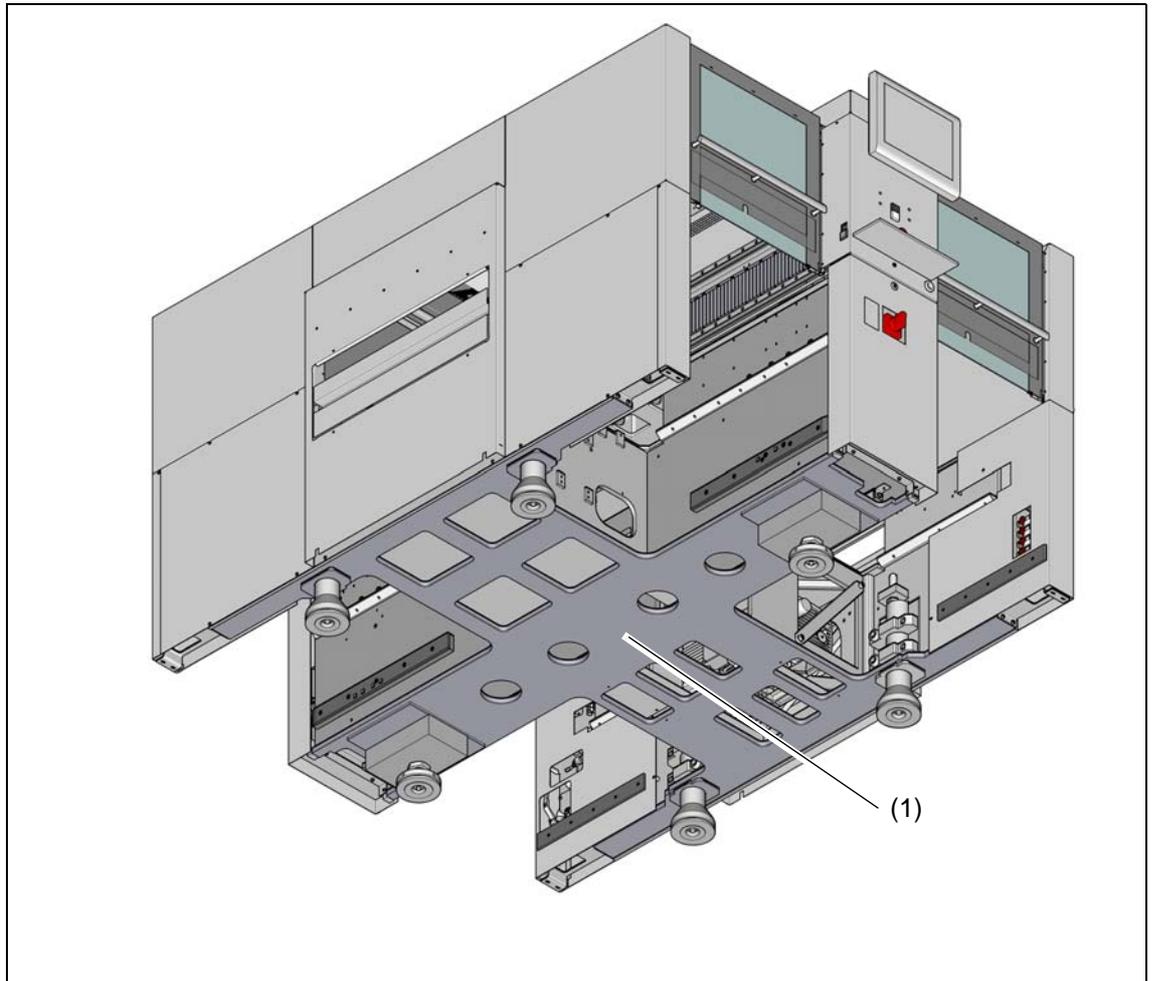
接触表面 - 与 PCB 传送方向呈正确角度的货叉 (示例为 SX4)
